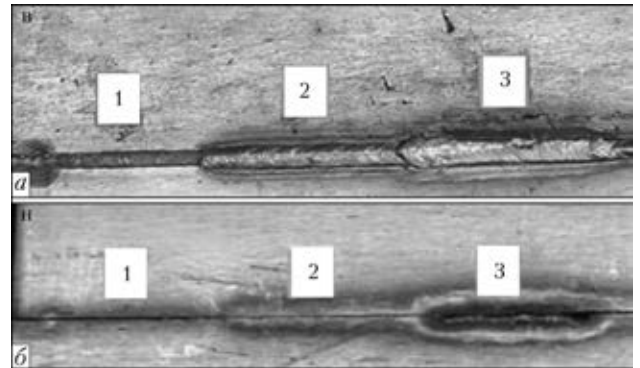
Внешний вид верхней (а) и нижней (б) стороны стыкового соединения образцов, выполненных из стали 08X17T ($\delta = 3,5$ мм): 1 — лазерная; 2 — плазменная; 3 — гибридная сварка
